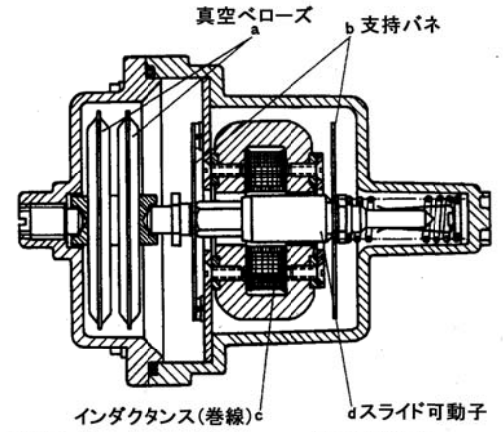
Saugrohrdruckfühler. a = Barometerdosen; b = Aufhängungsfedern; c = Induktivität; d = verschiebbarer Anker.
